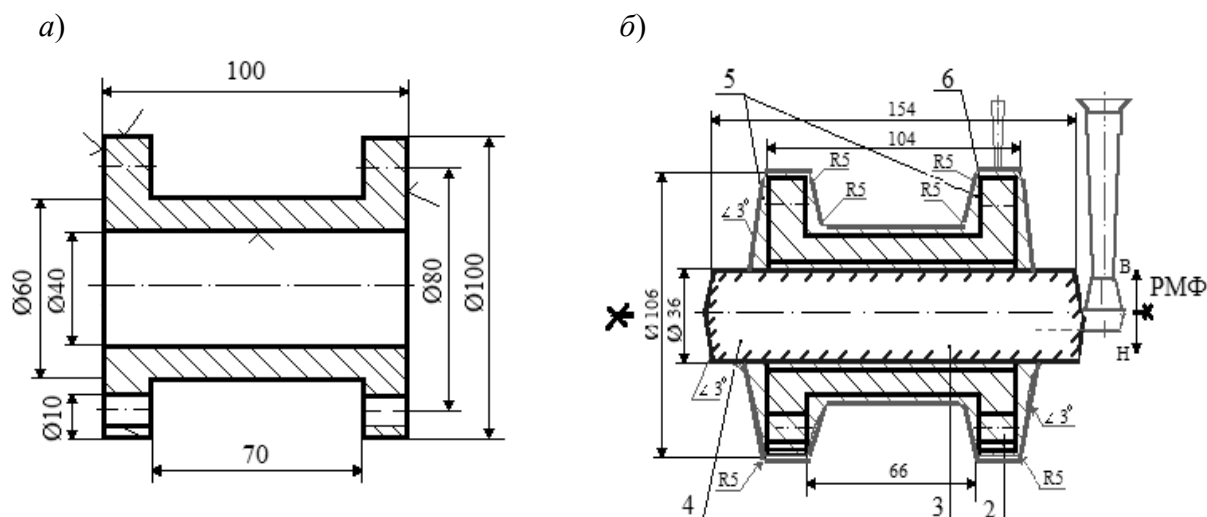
Эскизы детали (а) и технологического чертежа отливки (б)
